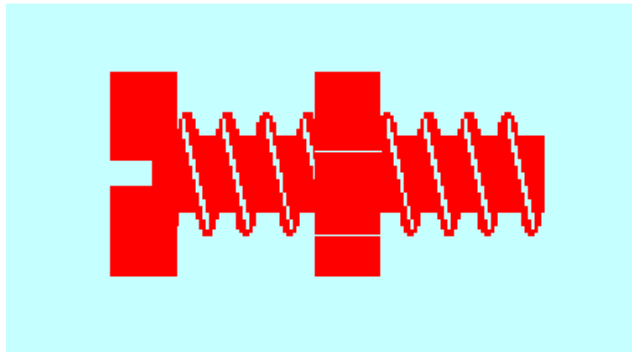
MECANISMO TORNILLO - TUERCA
